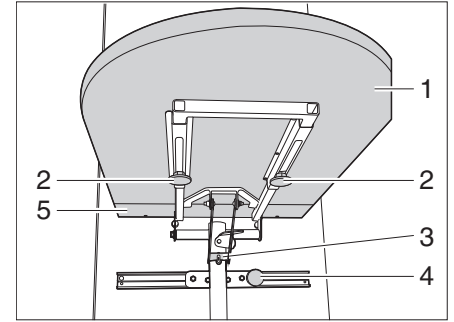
Mesa plegable, alojamiento del pie de apoyo
